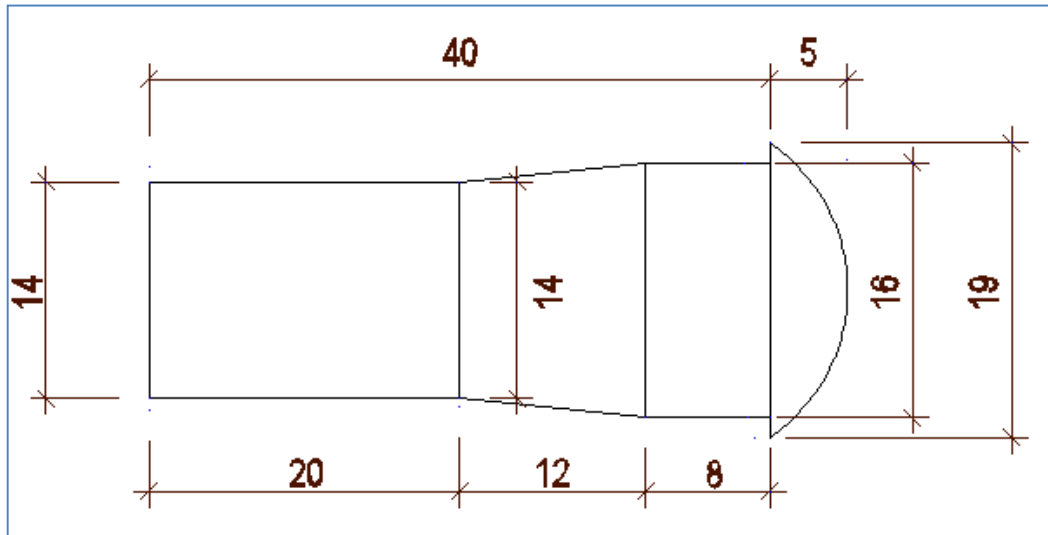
Detalle despiece pieza No.13 modelo 3 tensión.
